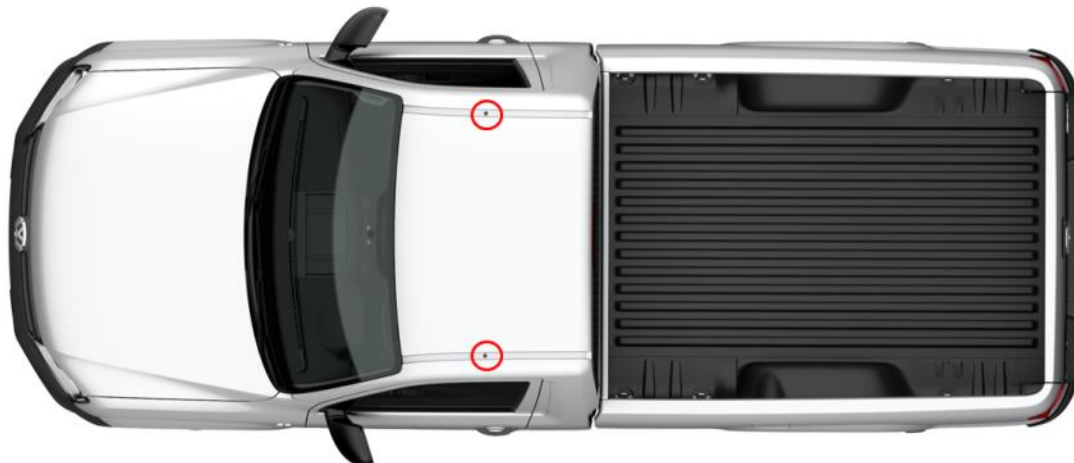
Anschraubpunkte Dachgepäckträger Amarok-SC (rot markiert)
